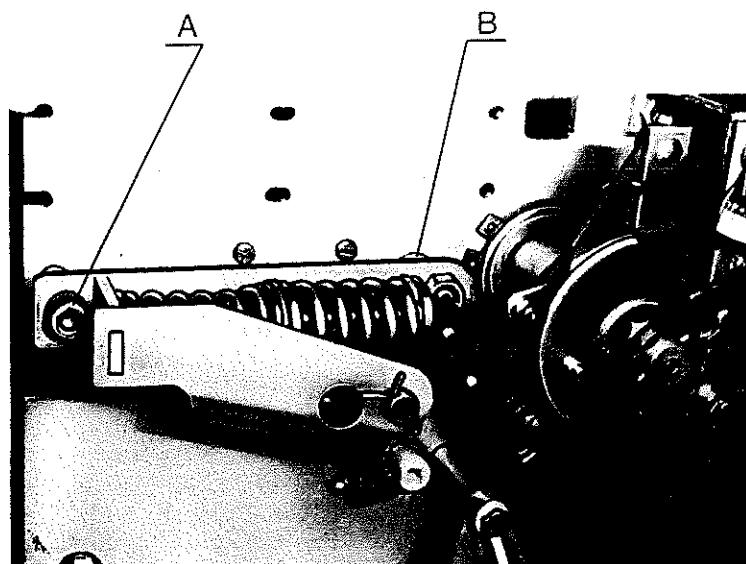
Montaggio dispositivo estrattore per l'apertura
